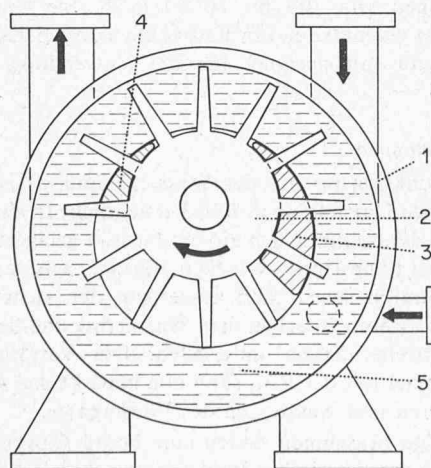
Prinzipbild einer Wasserringpumpe; 1 Gehäuse, 2 Rotor, 3 Ansaugöffnung, 4 Austrittsöffnung, 5 Wasserring (Maschinenfabrik Burckhardt AG, Basel)
